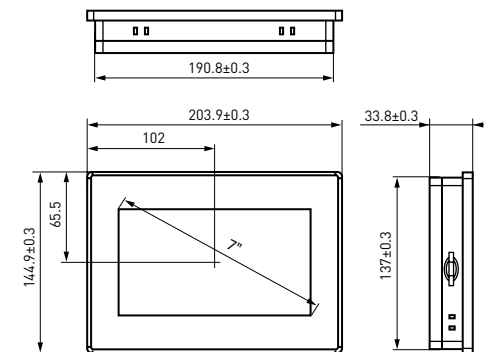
Габаритные размеры RSC-7 и RSC-7E
